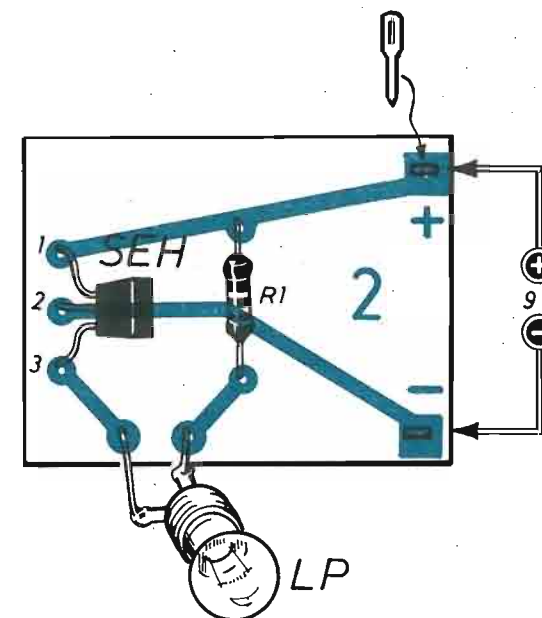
Schema pratico dell'interruttore elettronico con memoria. La basetta supporto è di forma rettangolare, delle dimensioni di 3,5 cm x 4,5 cm.
